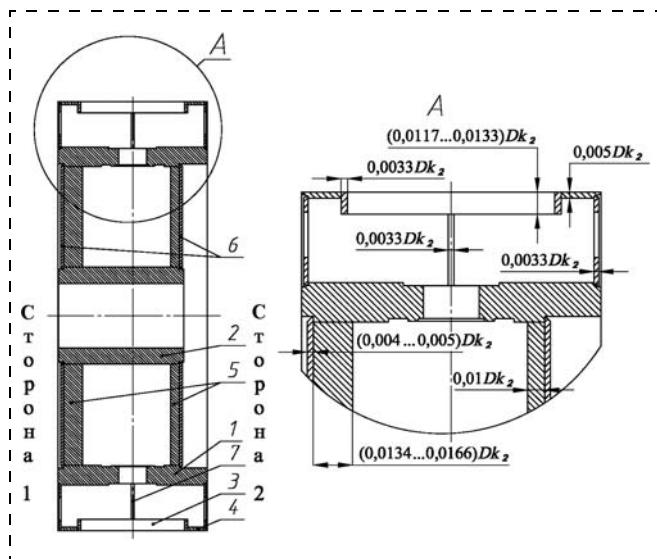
Параметрическая модель корпуса рабочего колеса:
